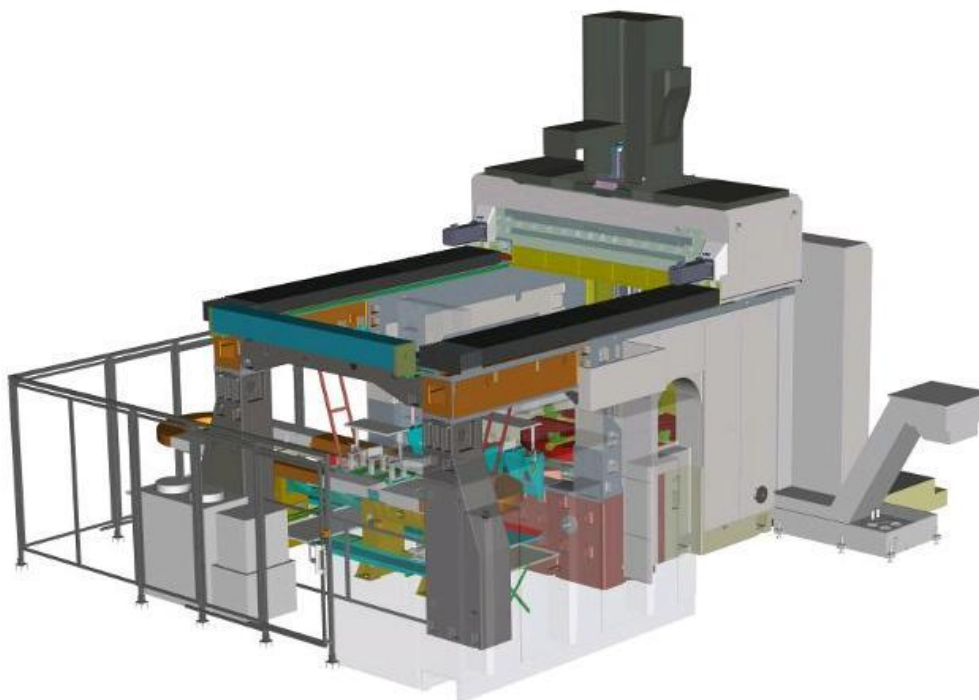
Stroj řady FRU od firmy TOS Kuřim[10]
